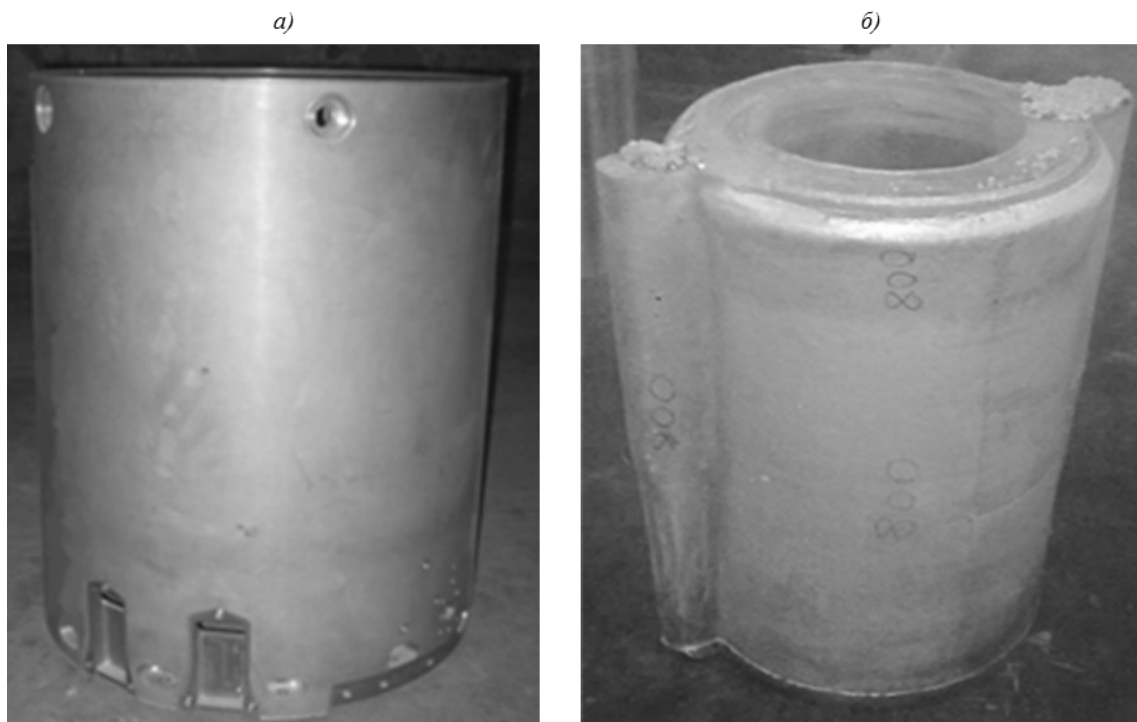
Внешний вид детали «Корпус отсека» (а) и отливки «Корпус отсека» (б)
